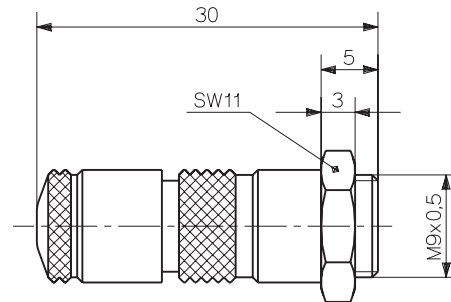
Stecker (Typ 1839) für Single-Wire Typen 6162AG... und E...
